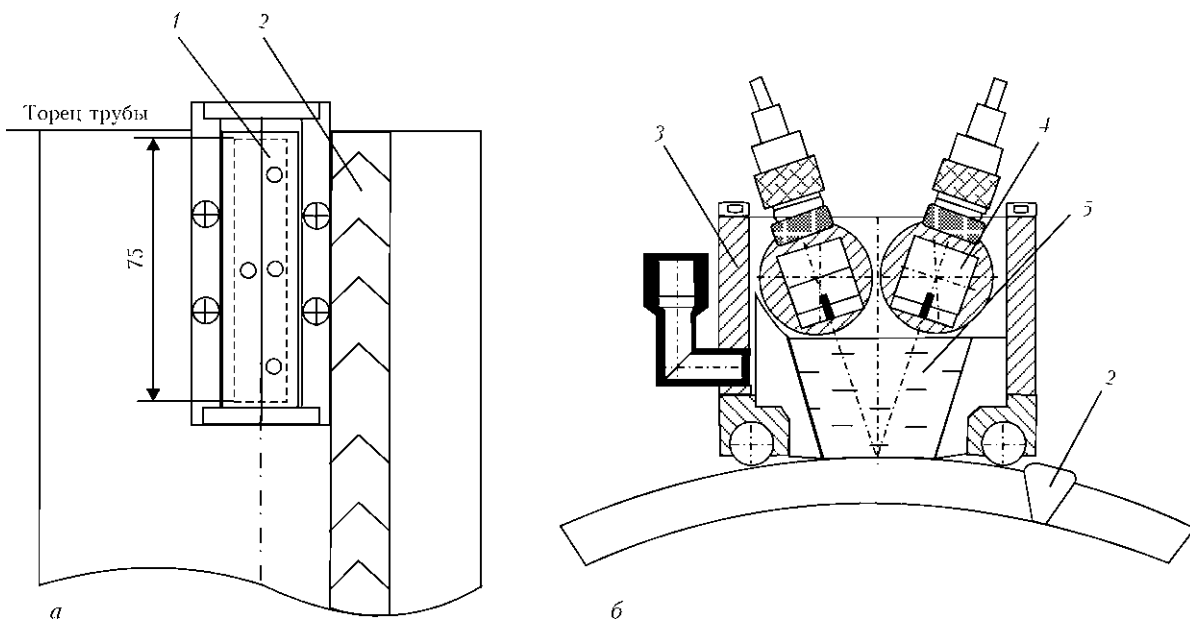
Акустические блоки установки НК 362МХ для контроля на расслоения (а) и на продольные дефекты (б): 1 — акустический блок со специализированным УЗ преобразователем для контроля на расслоения; 2 — сварной шов контролируемой трубы; 3 — локально-иммерсионный акустический блок для контроля на продольные дефекты с десятью УЗ преобразователями (угол ввода ультразвука в металл 45°); 4 — иммерсионный УЗ преобразователь для контроля на продольные дефекты; 5 — локально-иммерсионная ванна (иммерсионная жидкость — вода)
